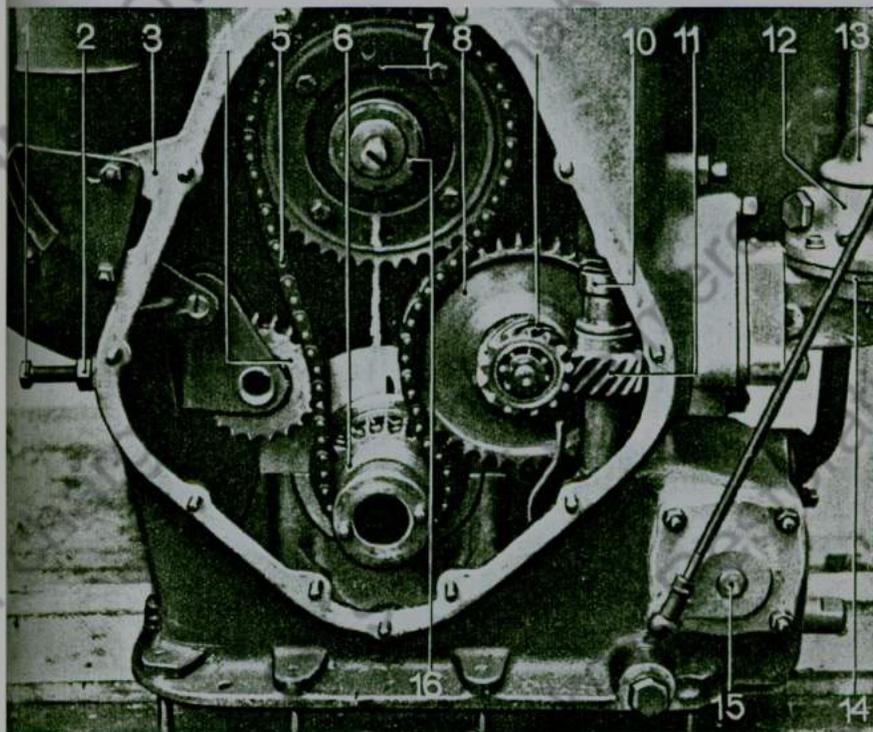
Motorsteuerungsantrieb und Steuerkettenspanner
